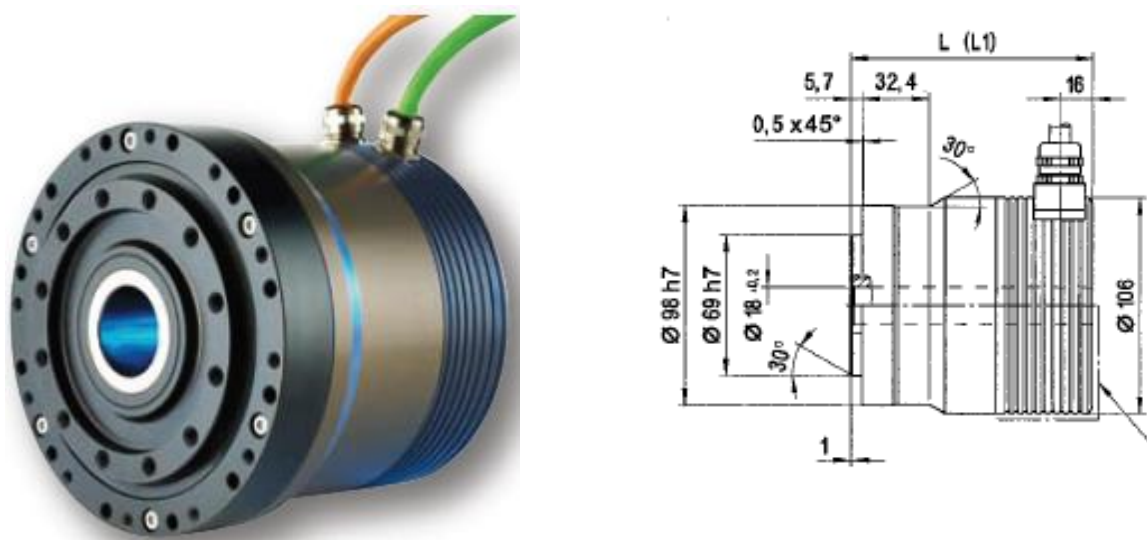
Сервопривод СНА-20А: внешний вид и габаритный чертеж
